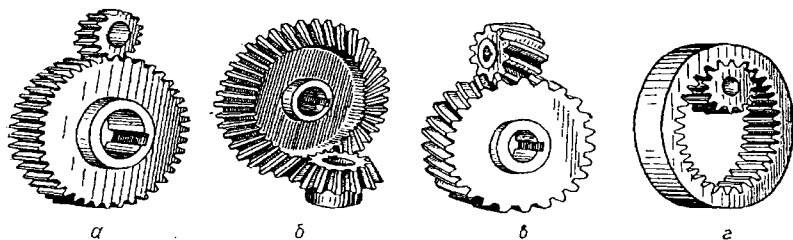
Виды зубчатых передач: а – цилиндрическая внешнего зацепления; б – коническая; в – винтовая; г – цилиндрическая внутреннего зацепления
